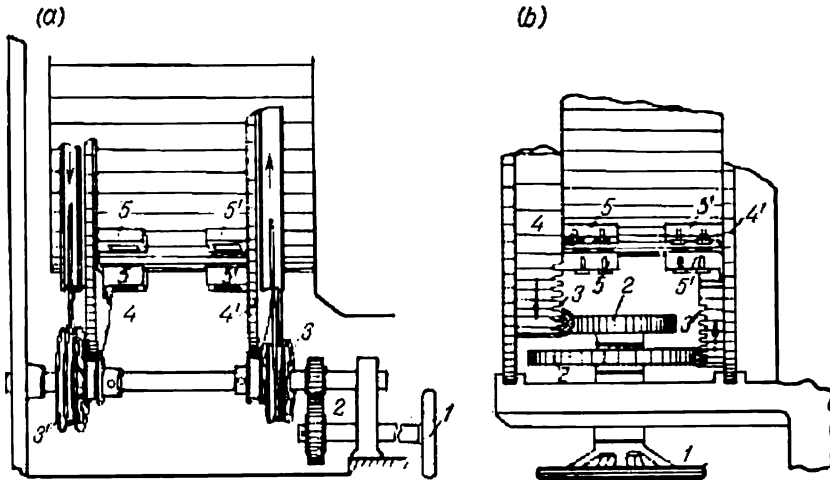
Dispositif à balais d'un moteur Schrage-Richter.
